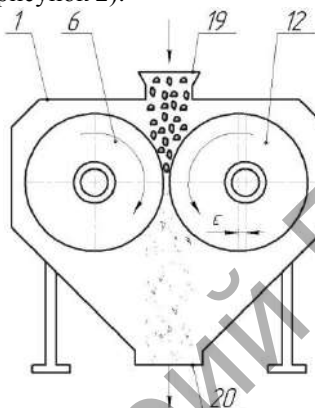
Схема вибровалкового измельчителя (вид сбоку)
